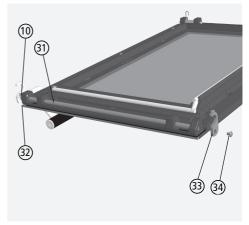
Poignée de porte : remontage de l'axe de poignée
